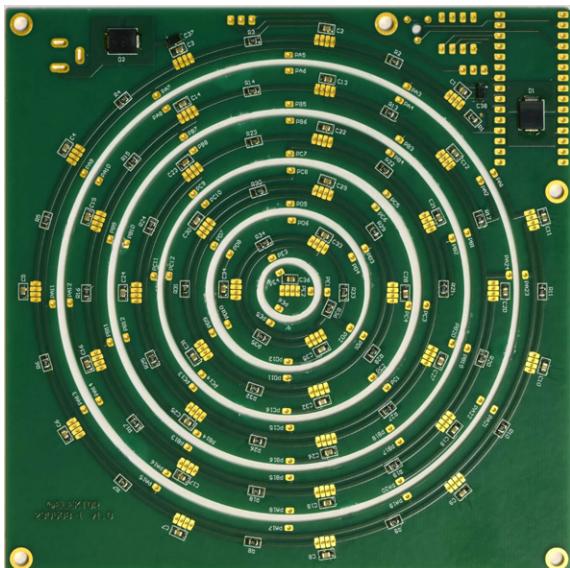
Tous les CMS sont soudés sur les faces arrière des PCB : R1...R36, C1...C38, D1 et D2.
